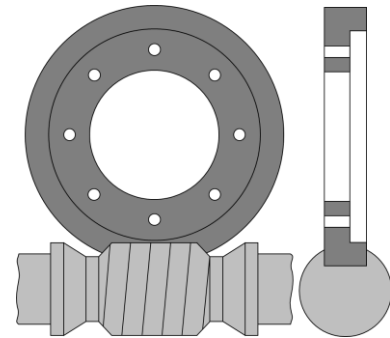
Schraubradgetriebe mit Zylinderschnecke und Stirnrad
